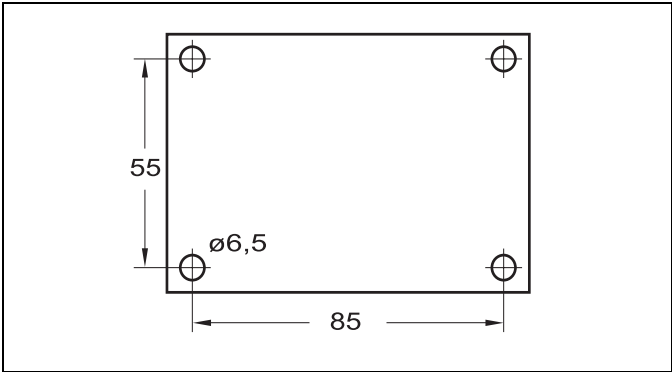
Lochbild für Ständer Umwälzpumpe U 4856
